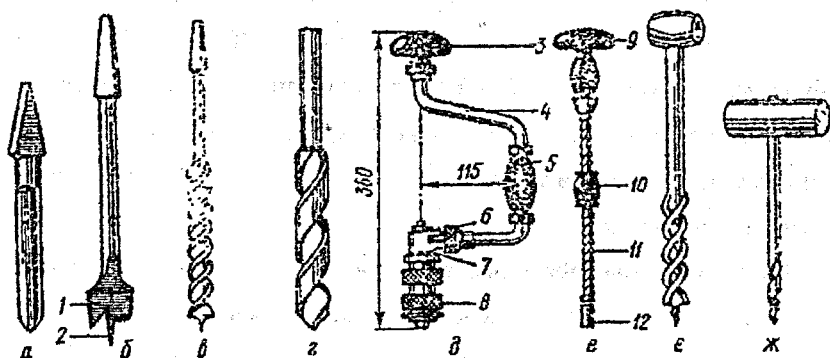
Свердла ручні та свердлильні інструменти:
